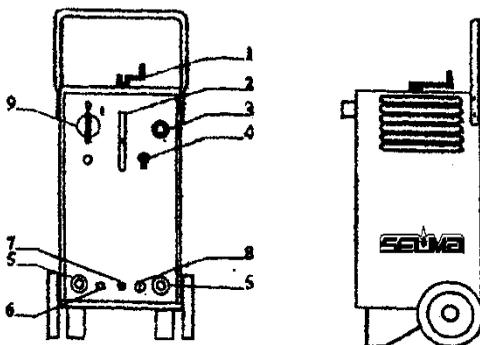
Общий вид установки УДГ 180: 1 - ручка регулирования сварочного тока; 2 - шкала установки тока; 3 - регулировка «Длительности продувки после сварки»; 4 - тумблер выбора режима «ММА-ТИГ»; 5 - токовые разъемы для подключения электроддержателя (ММА режим сварки покрытым-электродом) или горелки (ТИГ) и кабеля с клеммой; 6 - вход газового тракта; 7 - выход газового тракта (ТИГ); 8 - разъем включения установки от кнопки на горелке (ТИГ); 9 - переключатель «Сеть».
